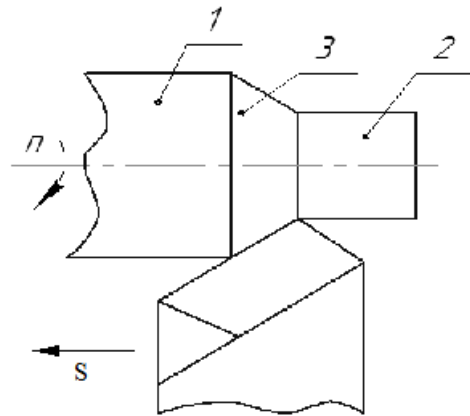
Поверхні на заготовці, яка оброблюється точінням
